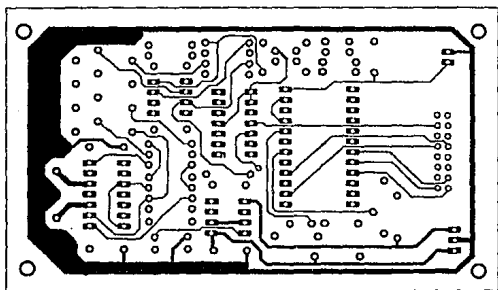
Cara de componentes del impreso de la etapa de adquisición.
